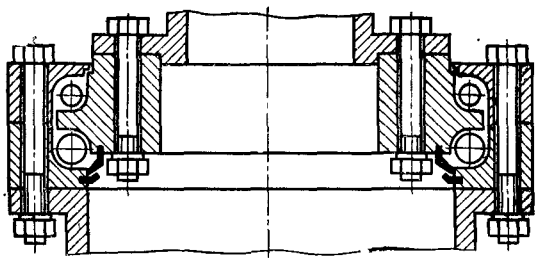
Двухрядный шариковый опорно-поворотный круг
